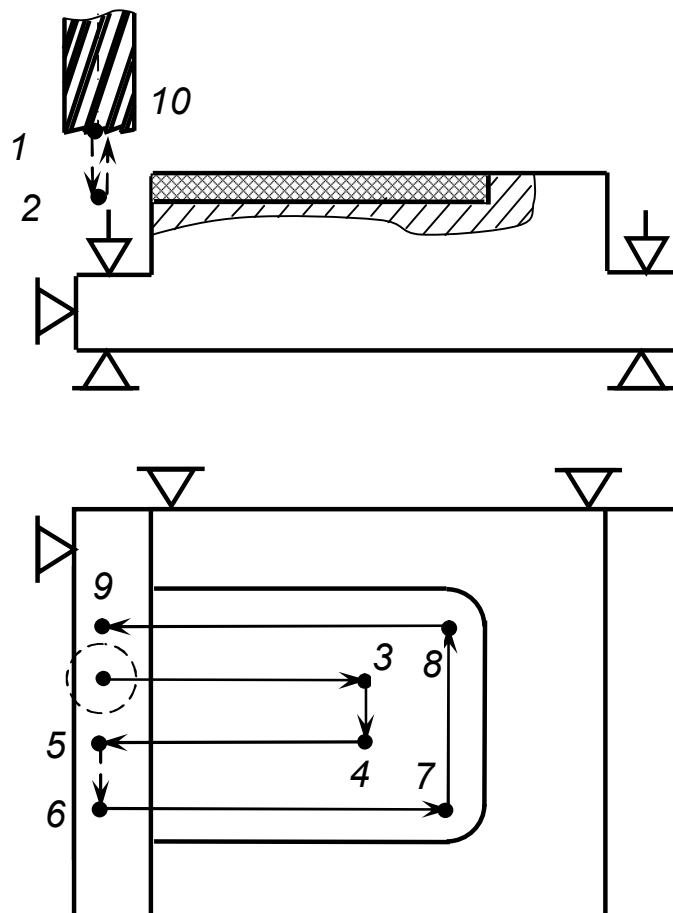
Схема фрезерної обробки напіввідкритої зони
